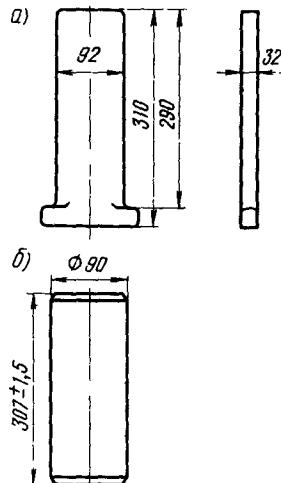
Детали соединения хвостовика корпуса автосцепки с тяговым хомутом
